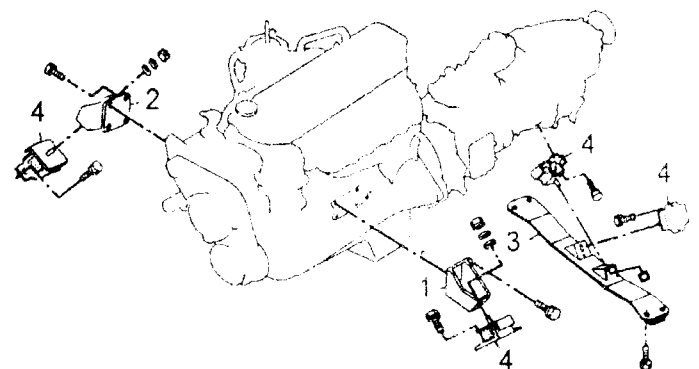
Soportes del motor y caja. 1. Soporte delantero izquierdo - 2. Soporte delantero derecho
